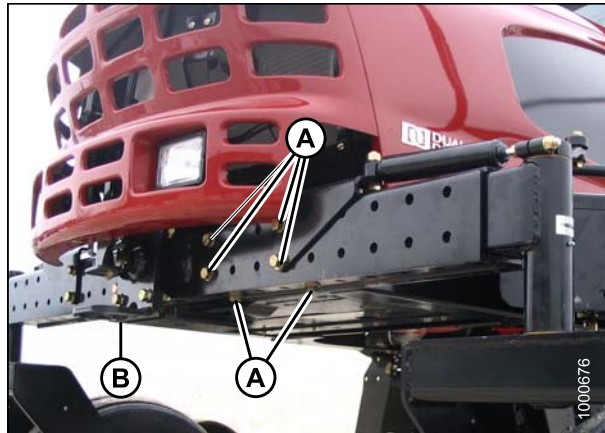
Удлинитель самоустанавливающихся колес
